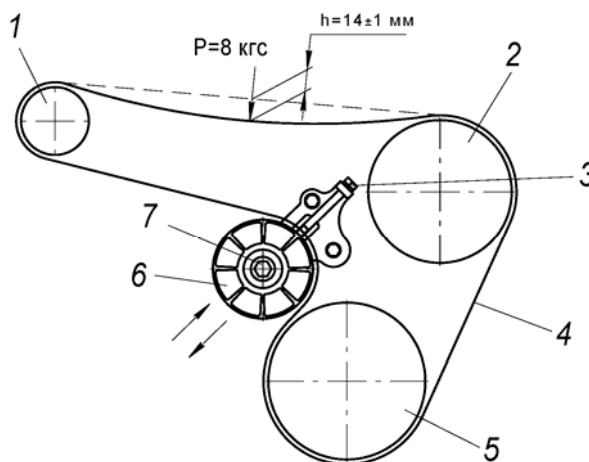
Схема натяжения ремня привода агрегатов:
